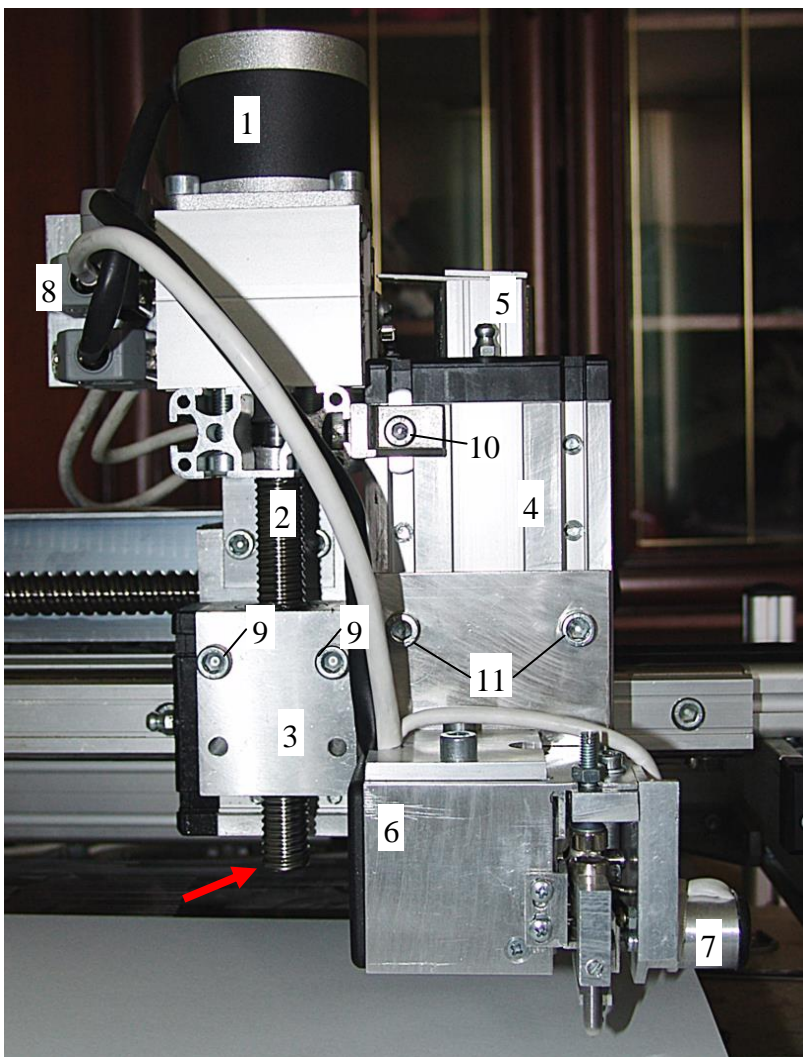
Крепление привода Z станка «График-ЗКП».
